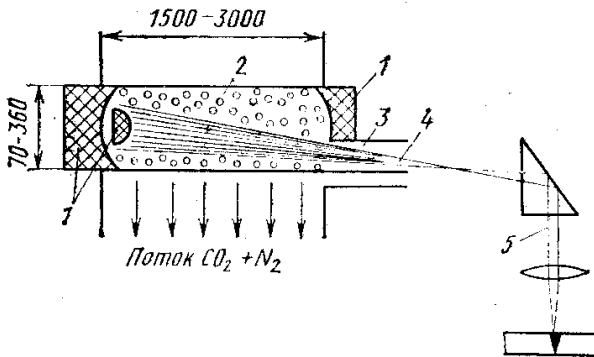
Схема установки для лазерной сварки с газовым лазером:
